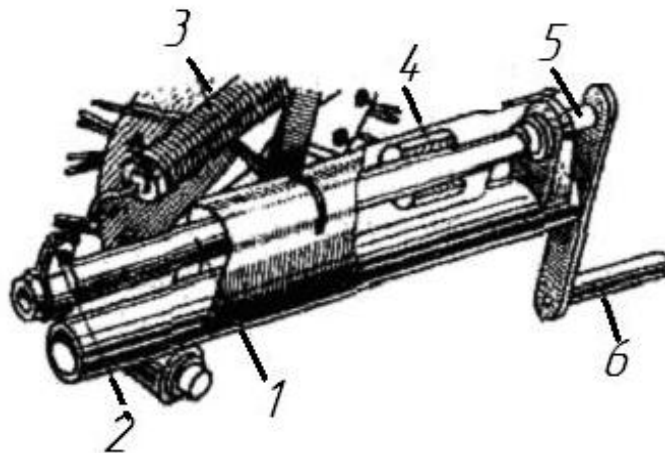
Механизм опускания пальцевых колес: 1 – труба; 2 – хомут; 3 – пружина; 4 – гайка; 5 – винт; 6 – рукоятка.
